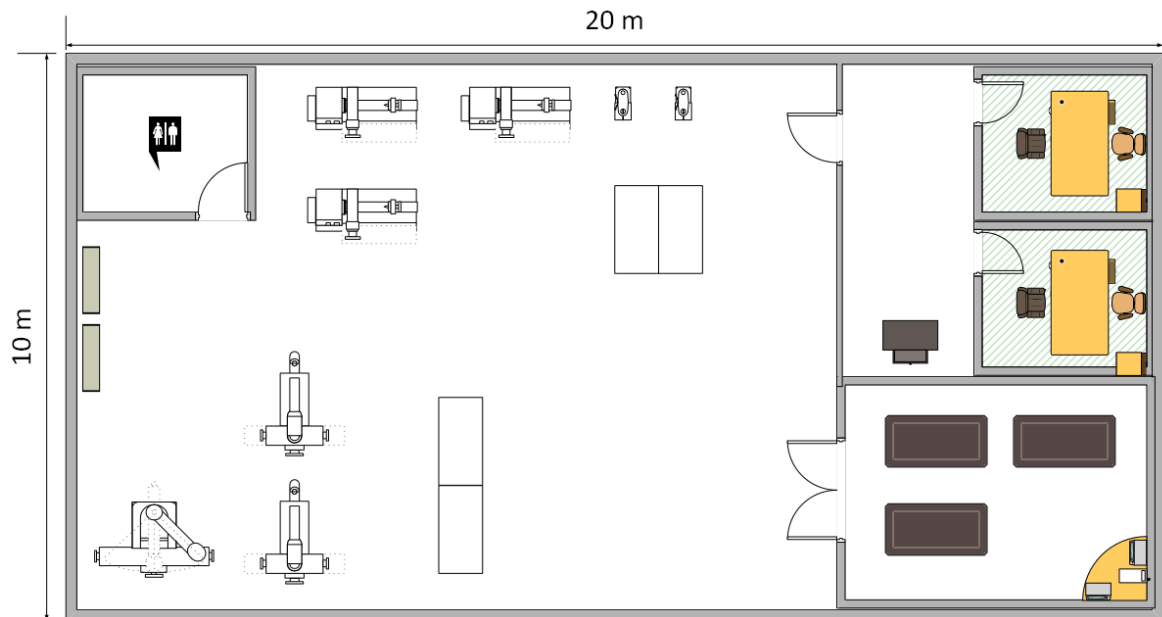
Layout de la planta actual. Fuente: Elaboración propia.
